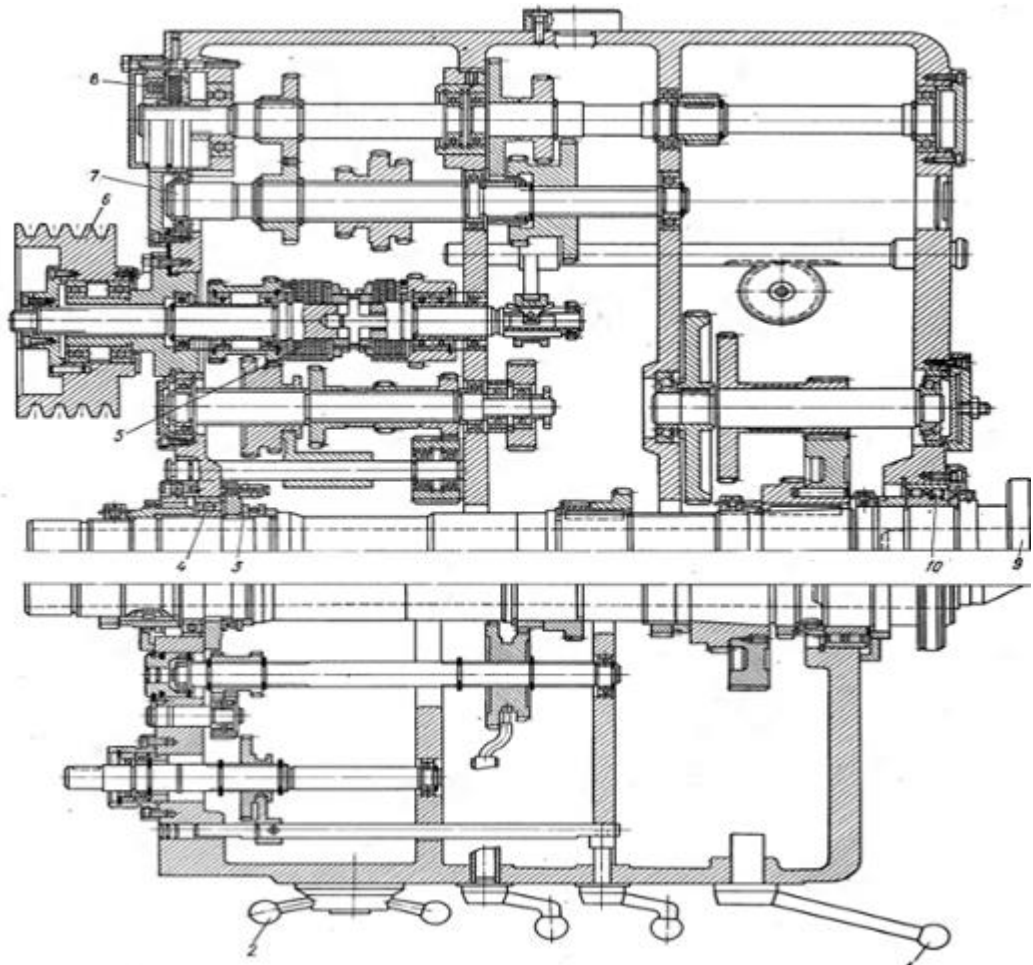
Схема коробки швидкостей верстату 1М63
